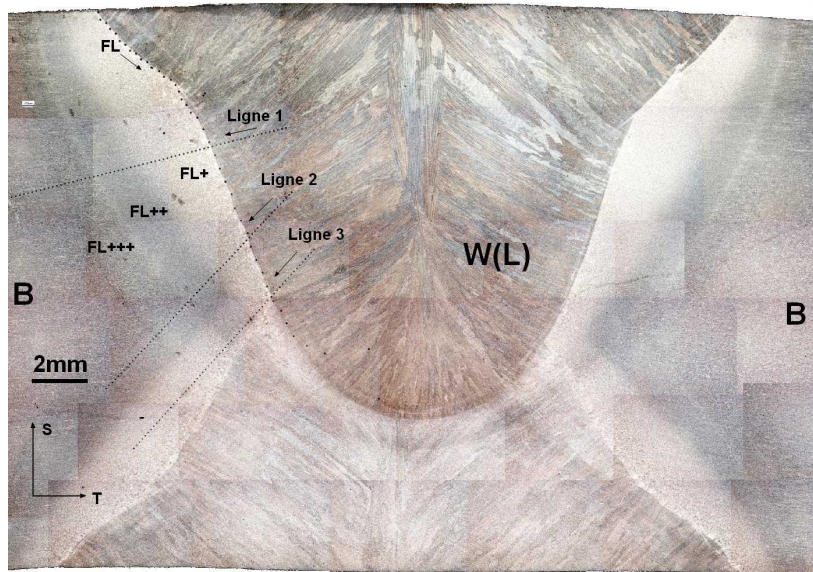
Coupe de la soudure longitudinale
